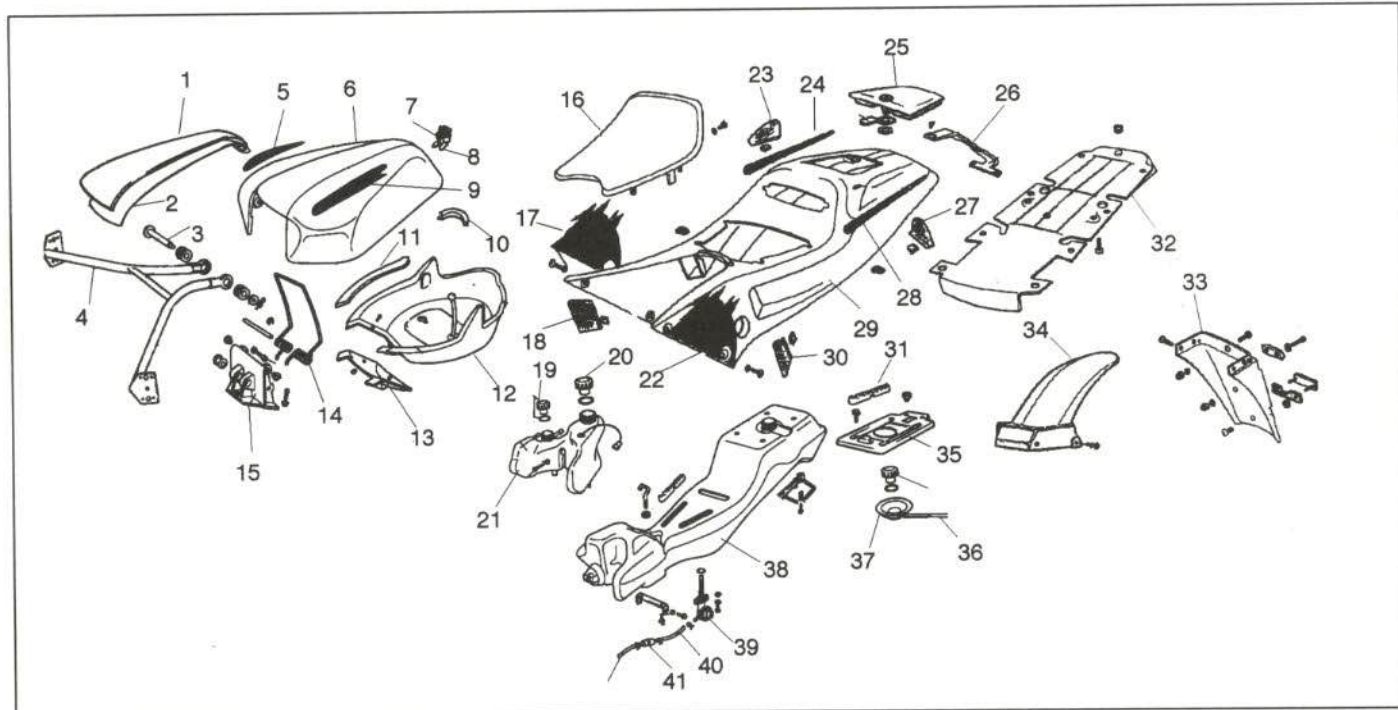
Despiece de las piezas exteriores de la parte trasera
